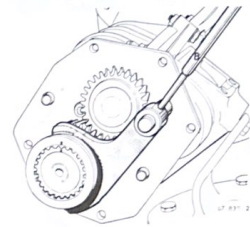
Sacando con un botador (B) el pasador de unión de la horquilla de mando con el eje.
